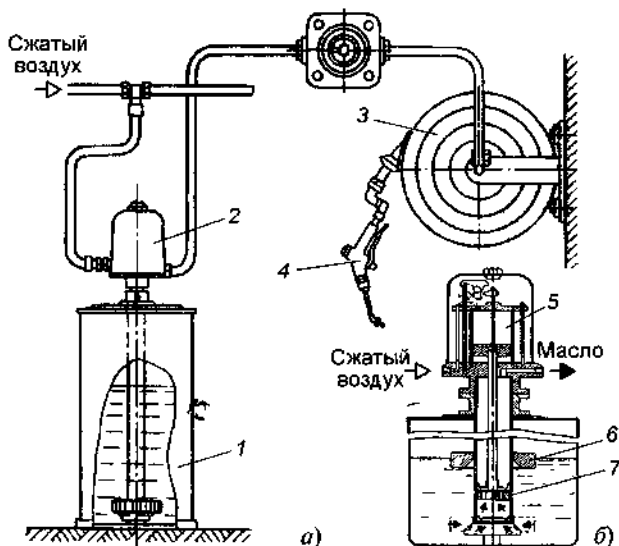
Пневматическое маслораздаточное устройство (а) с пневматическим насосом 3141 (б): 1 — бак; 2 — масляный насос; 3 — барабан со шлангом; 4 — раздаточный пистолет; 5 — пневматический двигатель; 6 — поплавок; 7 — насос
